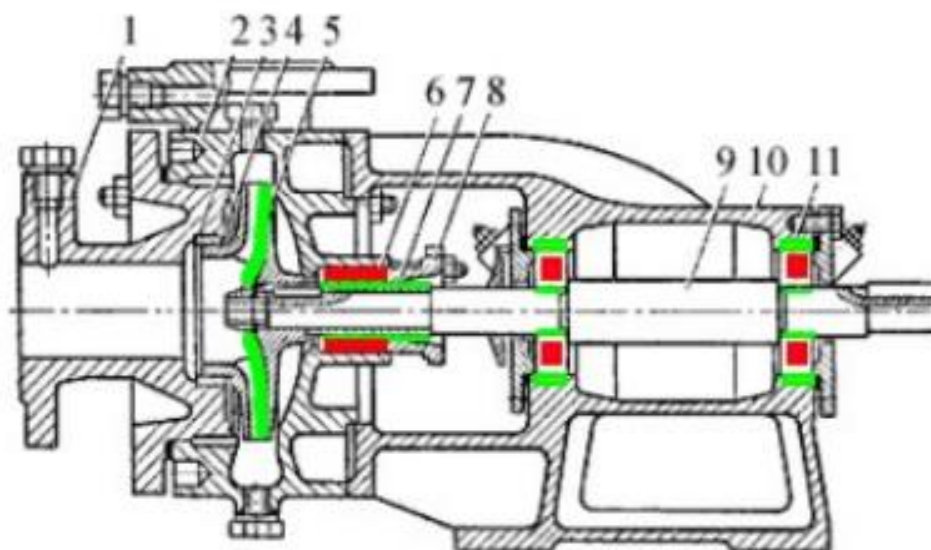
Типовая схема центробежного насоса: 1 – крышка; 2 – корпус; 3 – уплотняющие кольца; 4 – рабочее колесо; 5 – гайка; 6 – набивка сальника; 7 – защитная втулка; 8 – крышка сальника; 9 – вал насоса; 10 – опорный кронштейн; 11 – шарикоподшипник
